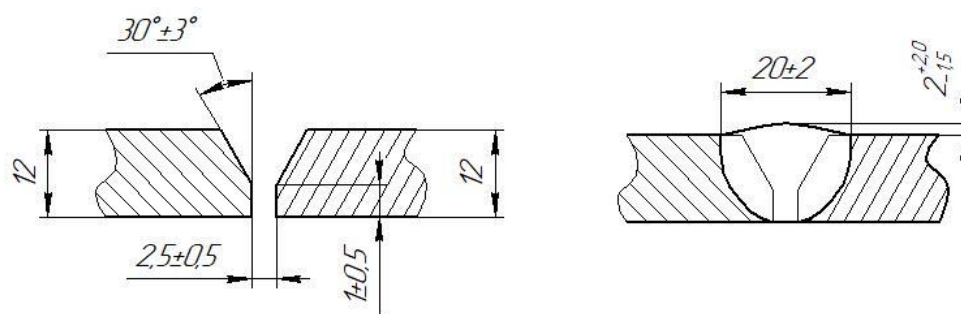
Форма подготовки кромок и форма сварного шва при выполнении продольного шва при соединении полуобечеек отвода
